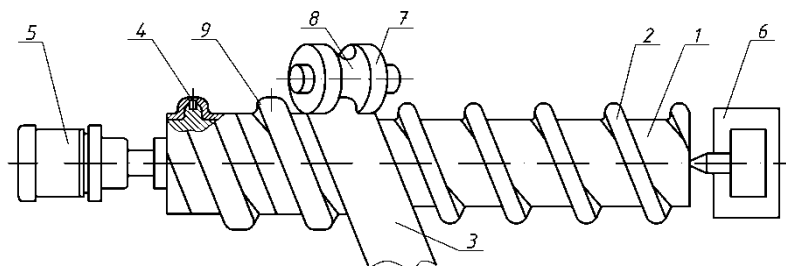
Спосіб виготовлення гвинтових заготовок
